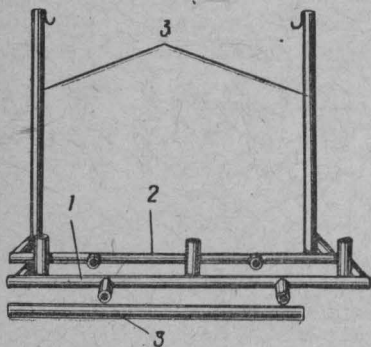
Металлическая рама для установки резервуара РЕ-6000:
